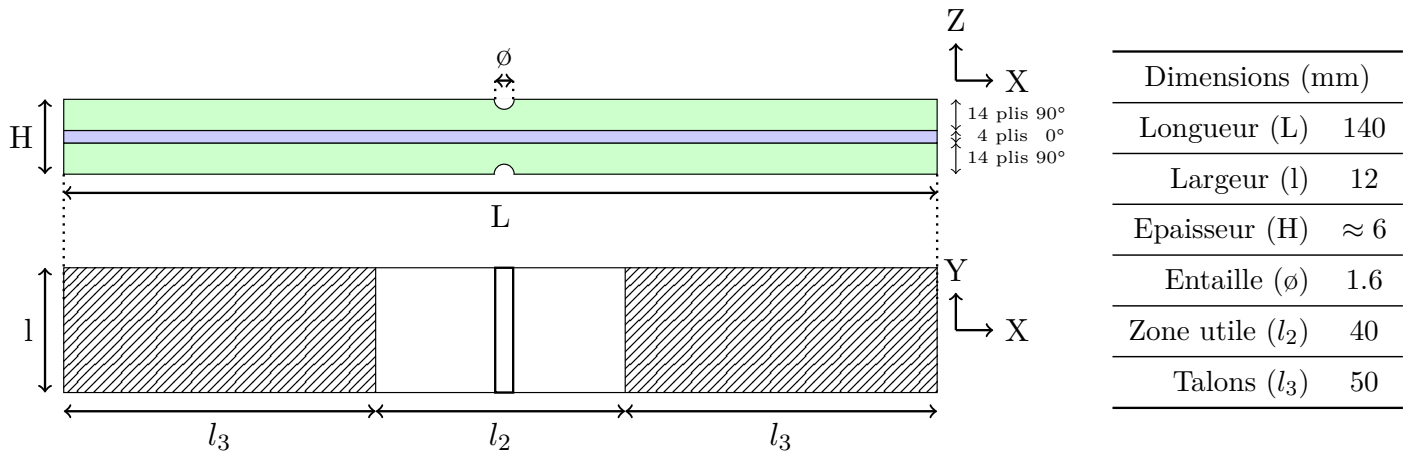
Géométrie des éprouvettes Double Entaille.
